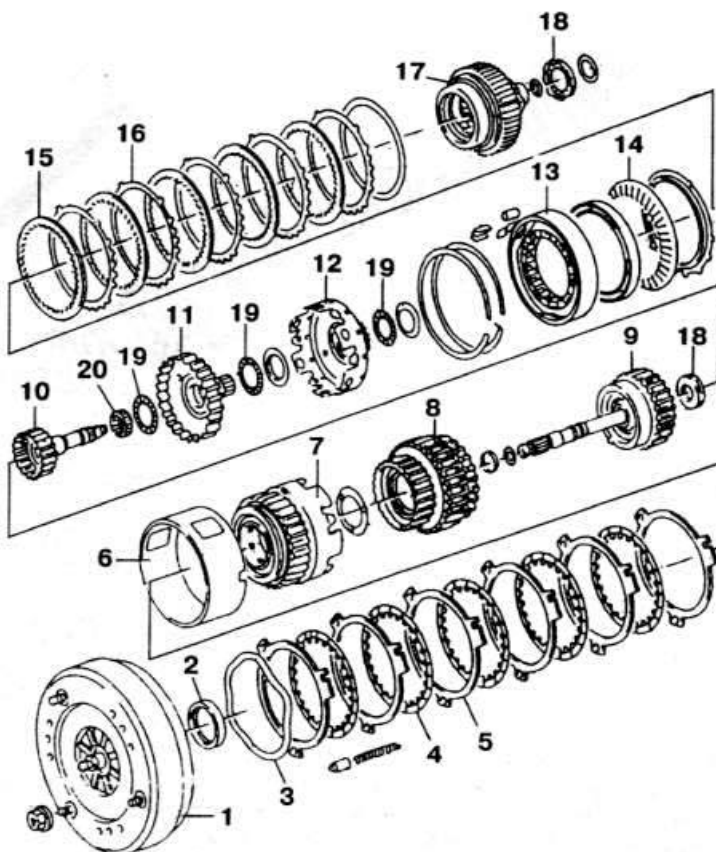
Детали автоматической коробки передач типа 01М:
